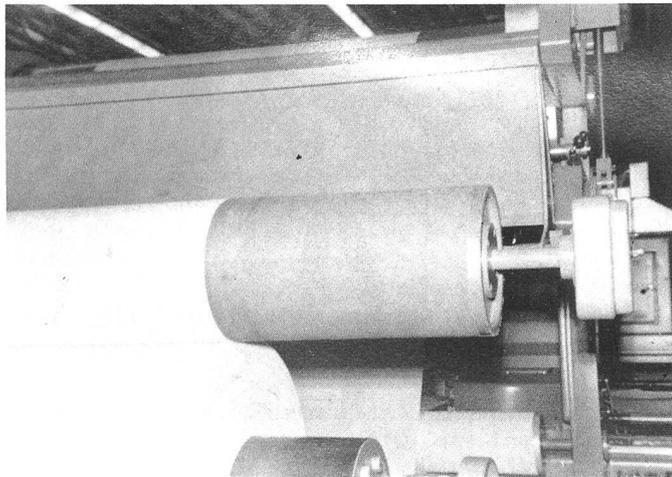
Wickler mit ausgeschwenkter Schutzhaube
